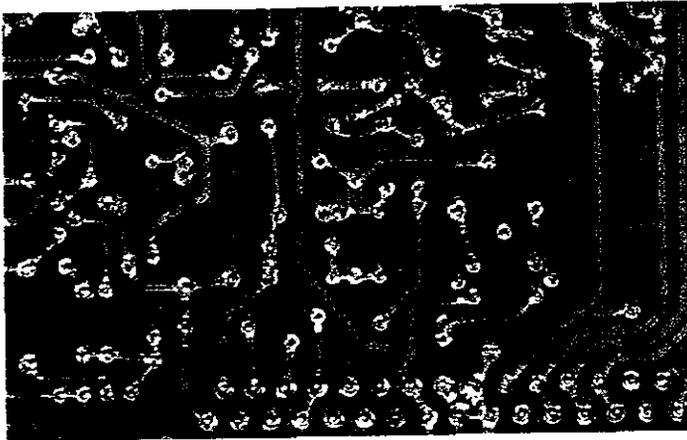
35 Remoción de revestimientos y soldaduras
